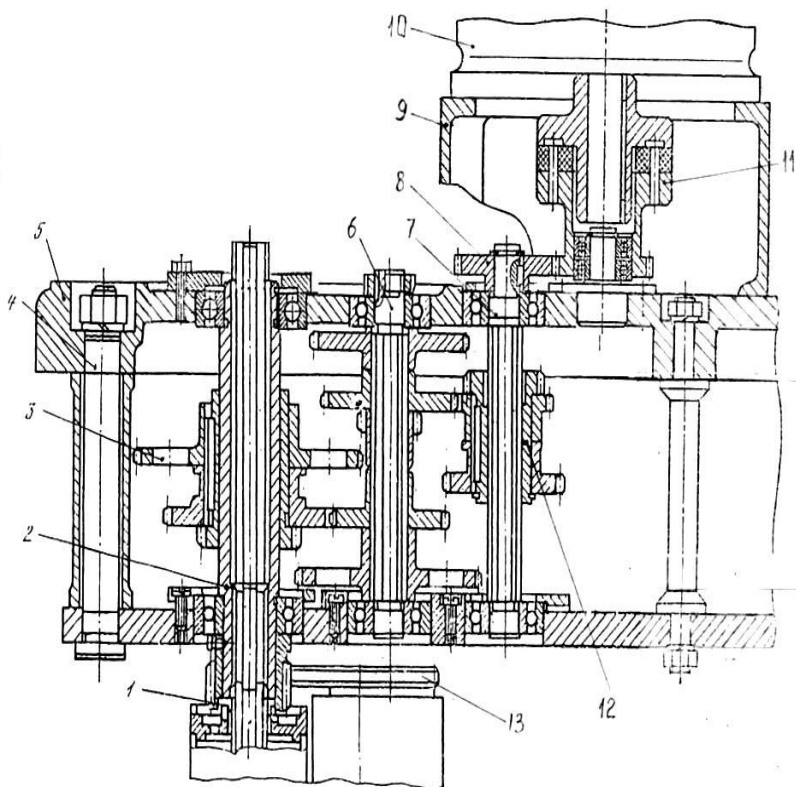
Коробка скоростей станка мод. 2Н118
